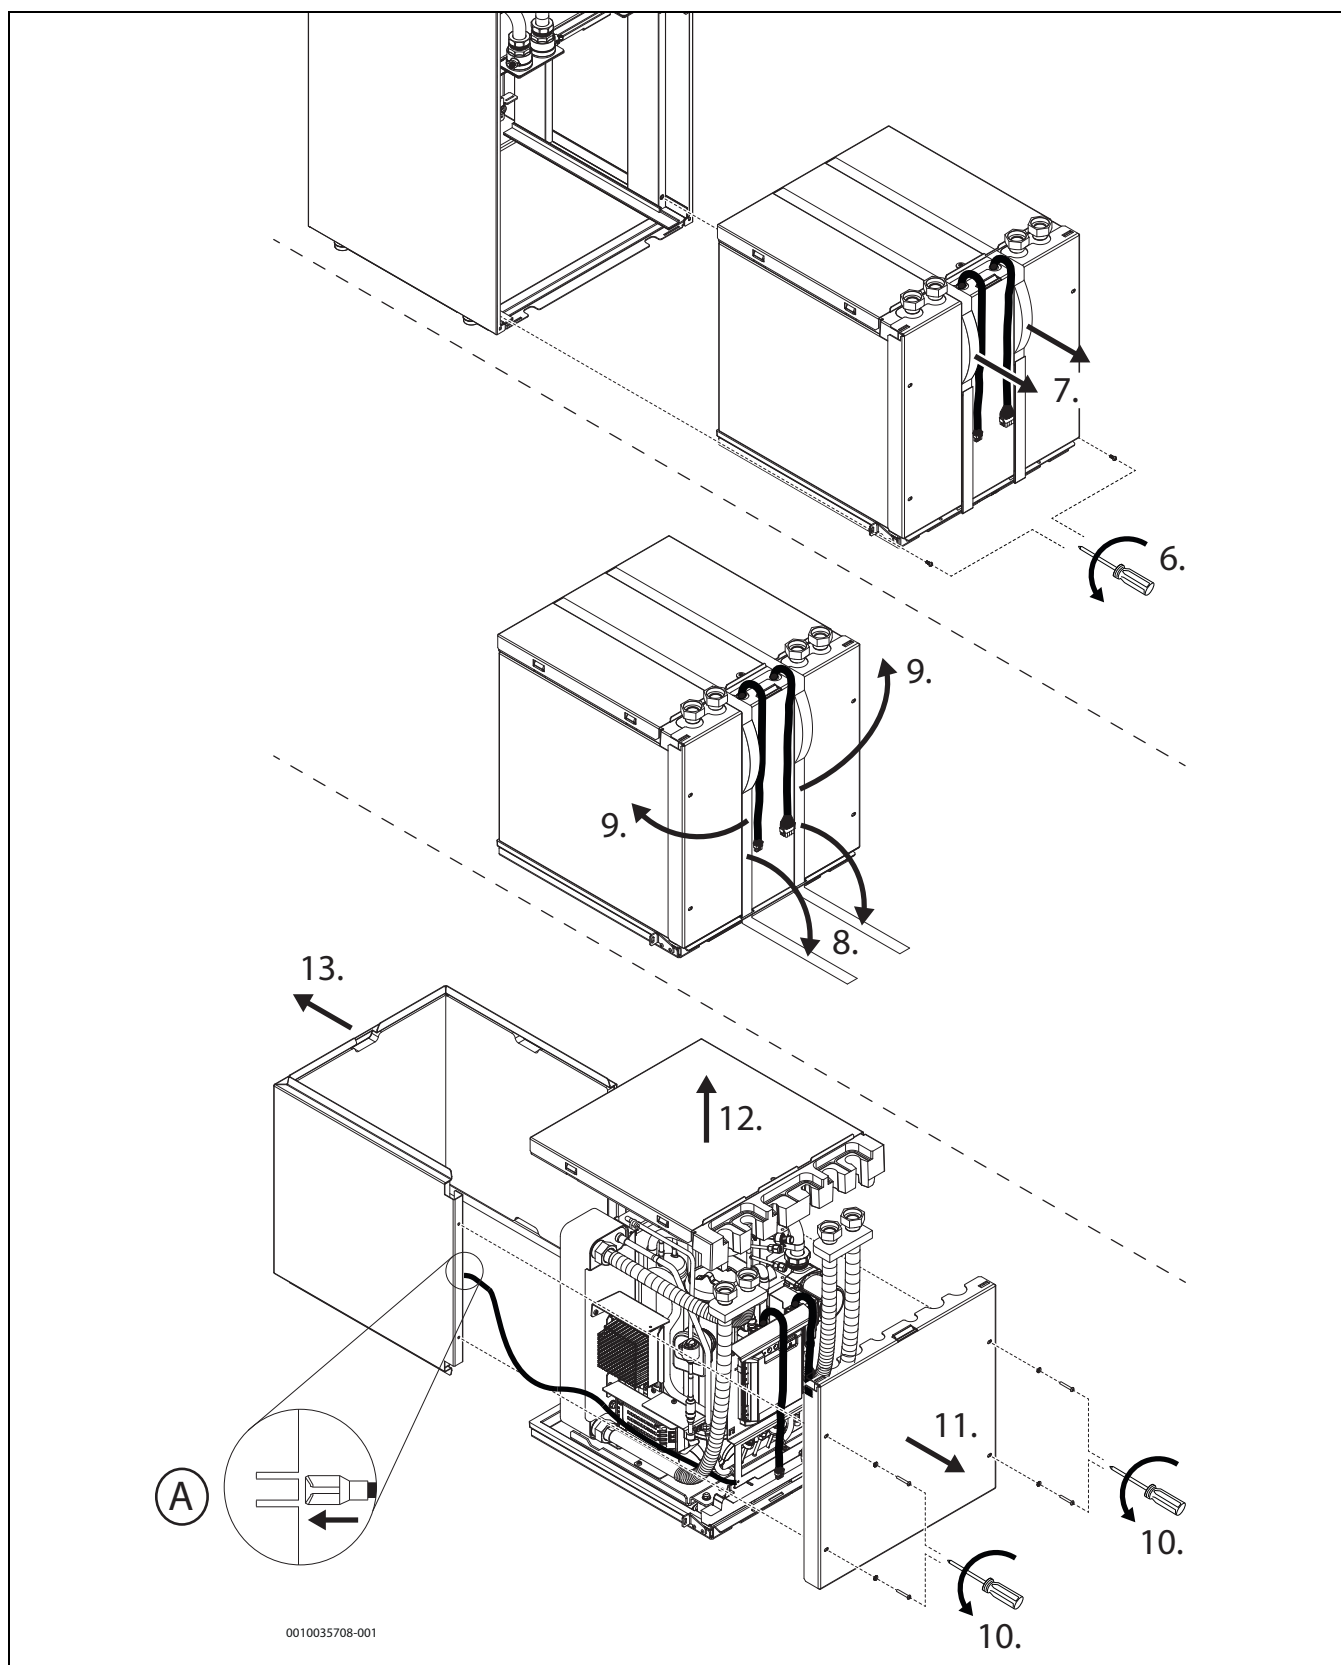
Přístupnost chladivového okruhu pro jednodušší instalační a údržbové práce
